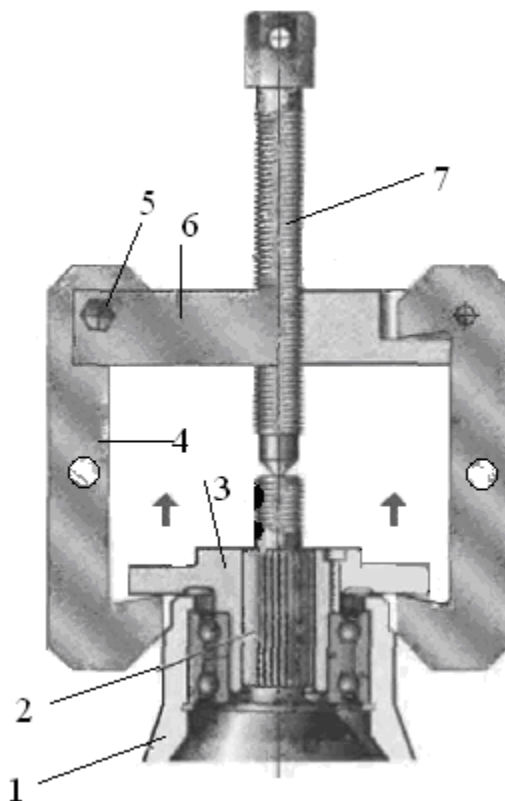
Конструкція пристосування для знімання маточини переднього колеса автомобіля
